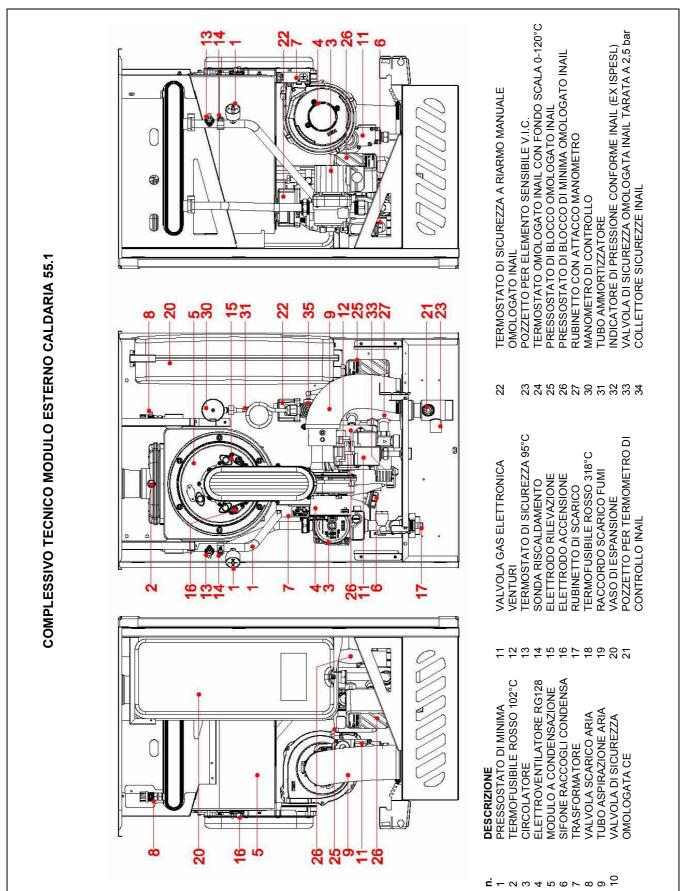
COMPLESSIVO TECNICO MODULO ESTERNO CALDARIA 55.1
